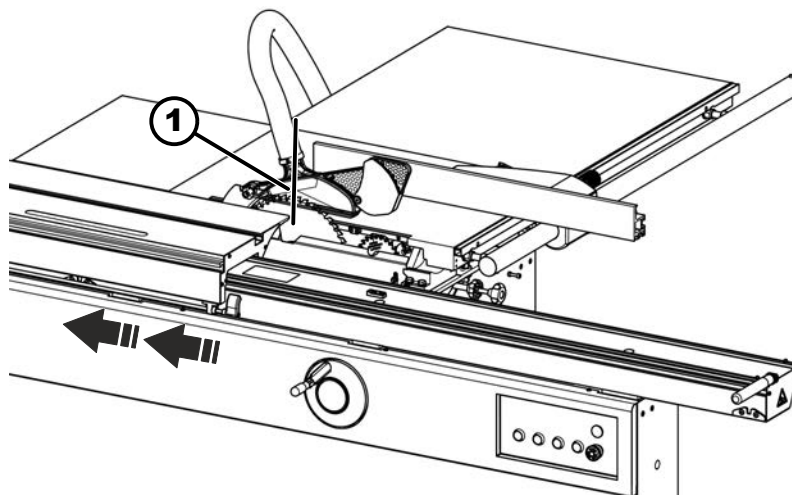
Alinear la jaula de rodamiento del carro deslizante
